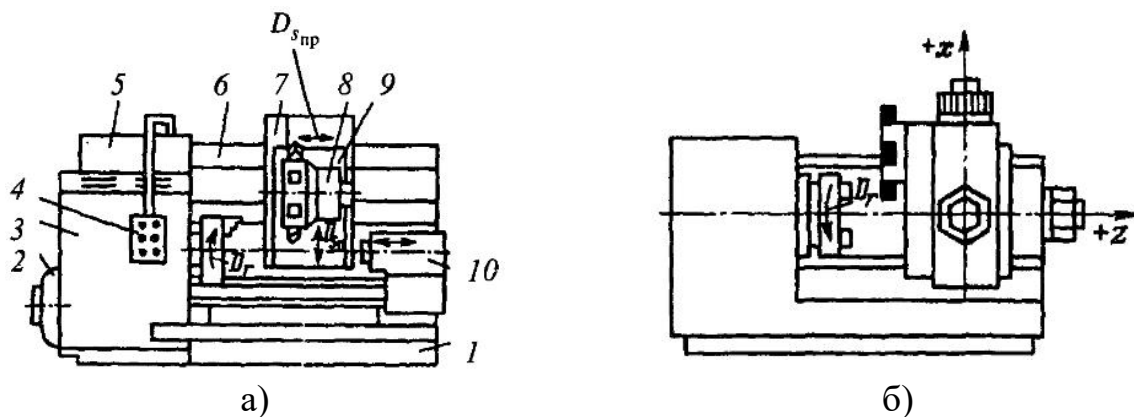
Загальні види токарних верстатів з ЧПК
